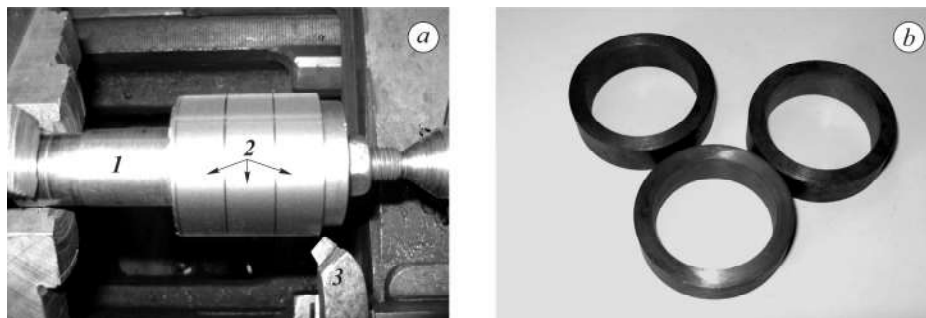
Зображення обробки (а) пакетного набору кілець (b) (1 – оправка; 2 – заготовки кілець для зразків; 3 – різець).
